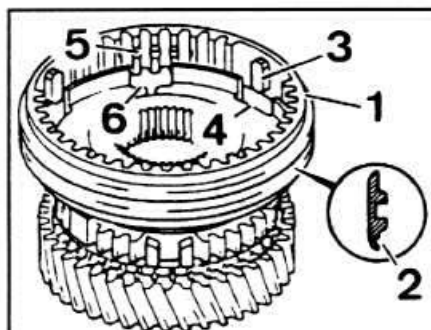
Установка скользящей муфты синхронизатора I и II передач:
